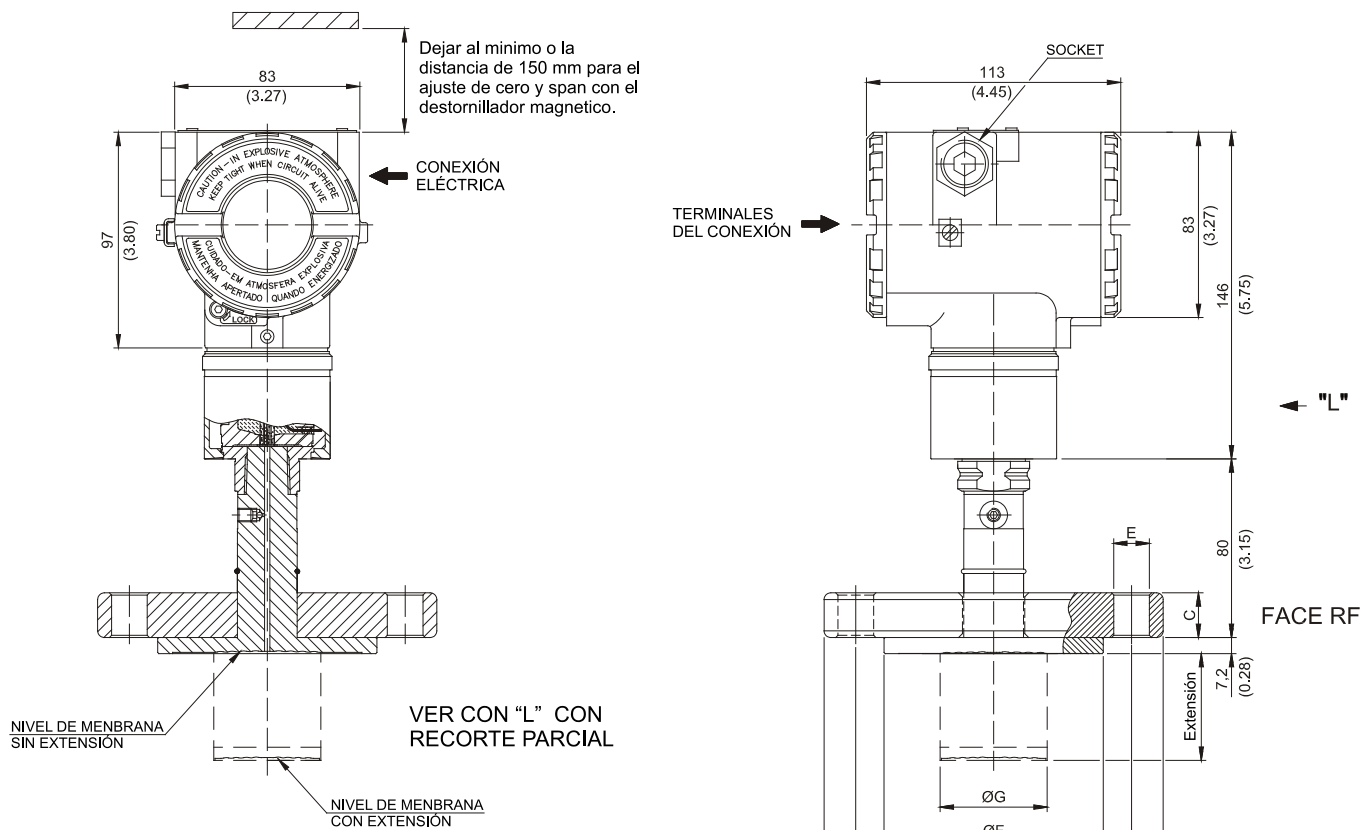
(b) – Diseño Dimensional de Montaje del LD290 – Sanitario Sin Extensión
